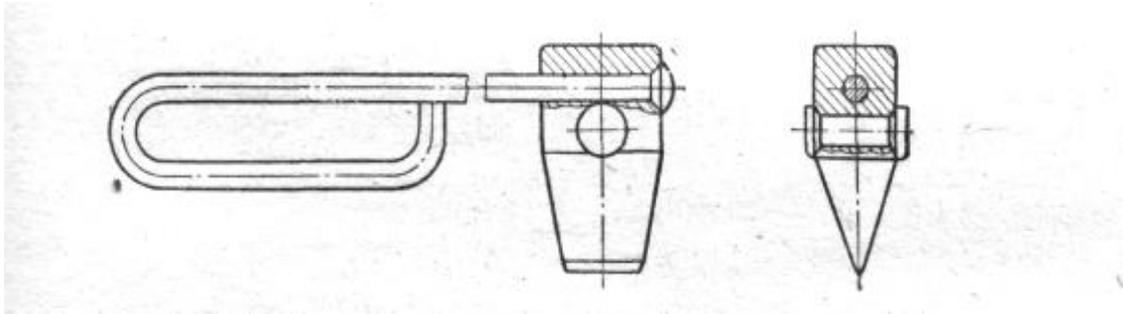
Паяльник для нагрева на стыковом сварочном аппарате
